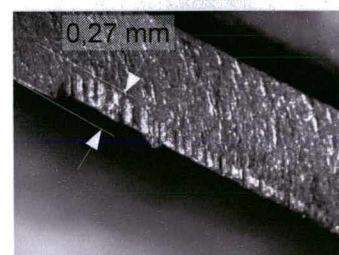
Imagens finais do flanco principal de ferramentas utilizadas nos ensaios de desgaste ED
